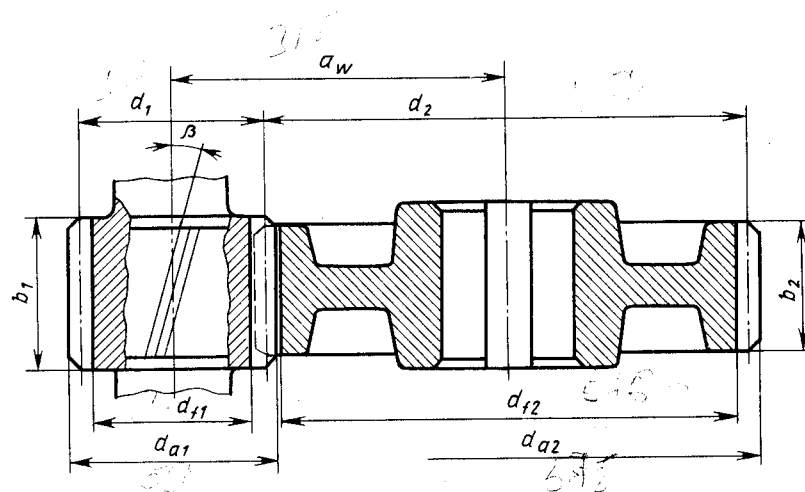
Геометрические параметры цилиндрической зубчатой передачи
